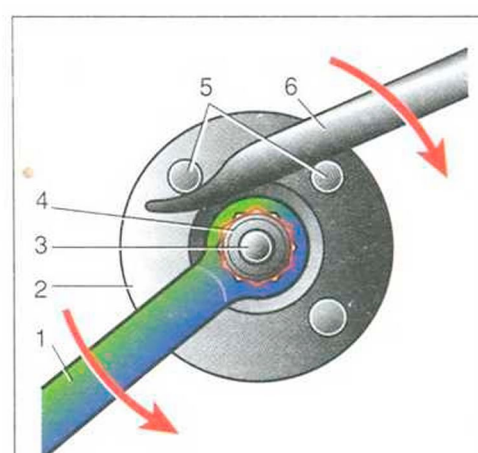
Способ отворачивания гайки ведущей шестерни: 1 - ключ; 2 - фланец; 3 - хвостик; 4 - гайка М16х1,5; 5 - болты М8; 6 - монтажная лопатка
